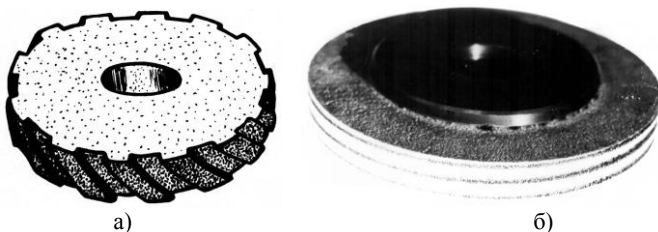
Абразивные шлифовальные круги, обеспечивающие непрерывный контакт с обрабатываемой деталью: прерывистый круг с наклонными пазами (а) и круг со спиральными канавками на рабочей поверхности (б)
